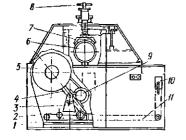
Устройство УРП-500 для резки пластмассовых труб диаметром до 315 мм: 1— основание; 2— тележка; 3— увел пориода; 4— маятник; 5— абразненые круг; 6— труба; 7— сменые приямы; 8— за-жимная рукоять; 9— электродвигатель; 10— рукоять привода тележки; 11— цепь перемещения тележки.
